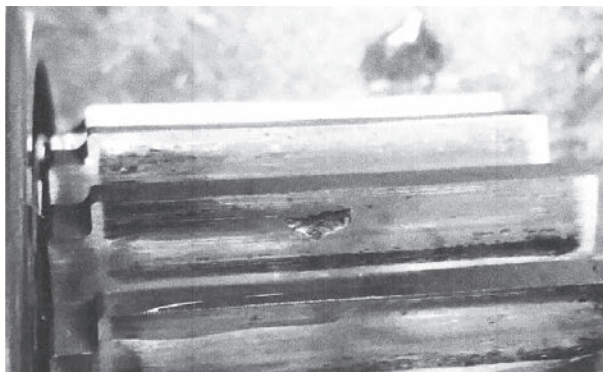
Питтинг на зубьях солнечной шестерни 3-го планетарного ряда
